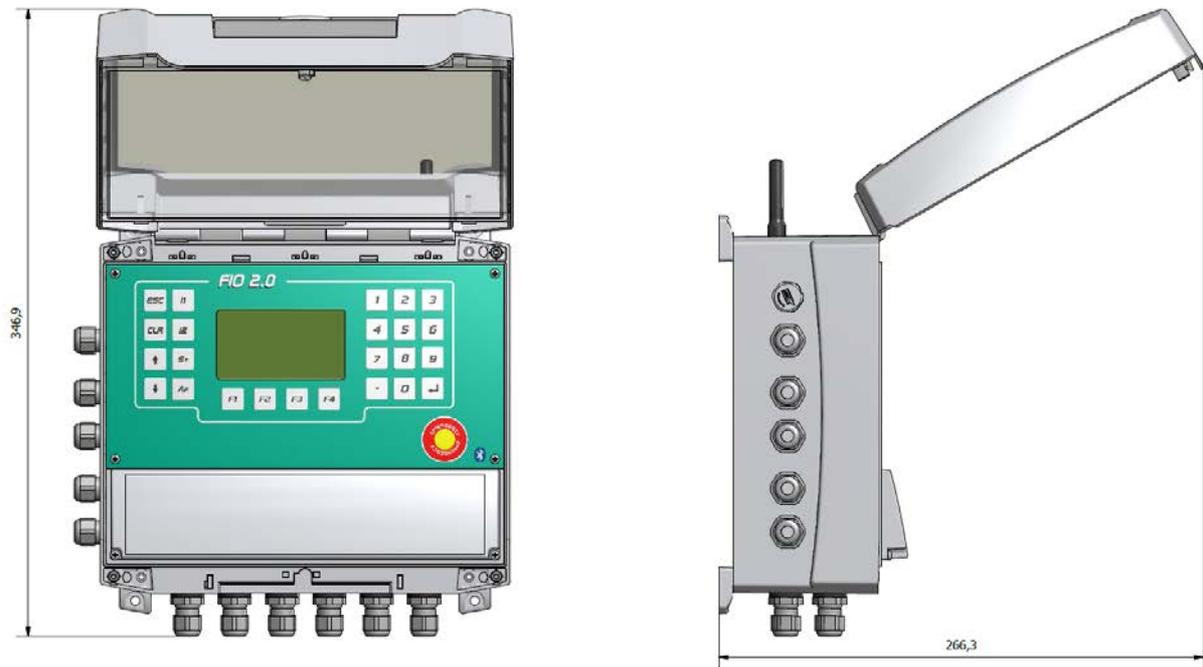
Обзорный вид устройства с открытой передней дверью
